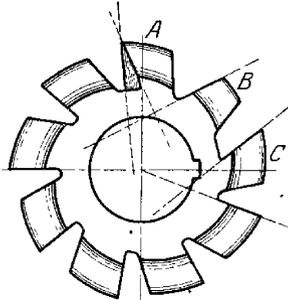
Fehler beim Schleifen hinterdrehter Fräser.
